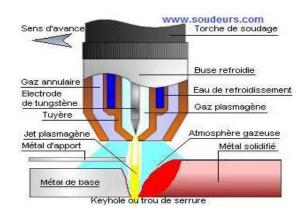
Principe de Soudage à l'arc plasma [15]
